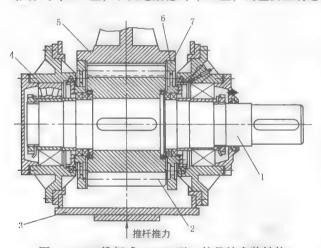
推杆式 (BFP 型) 的悬挂安装结构 1—末级输入轴; 2—末级小齿轮; 3—悬挂架体; 4—轴承盒; 5—末级大齿轮; 6—辊子; 7—外轨道
